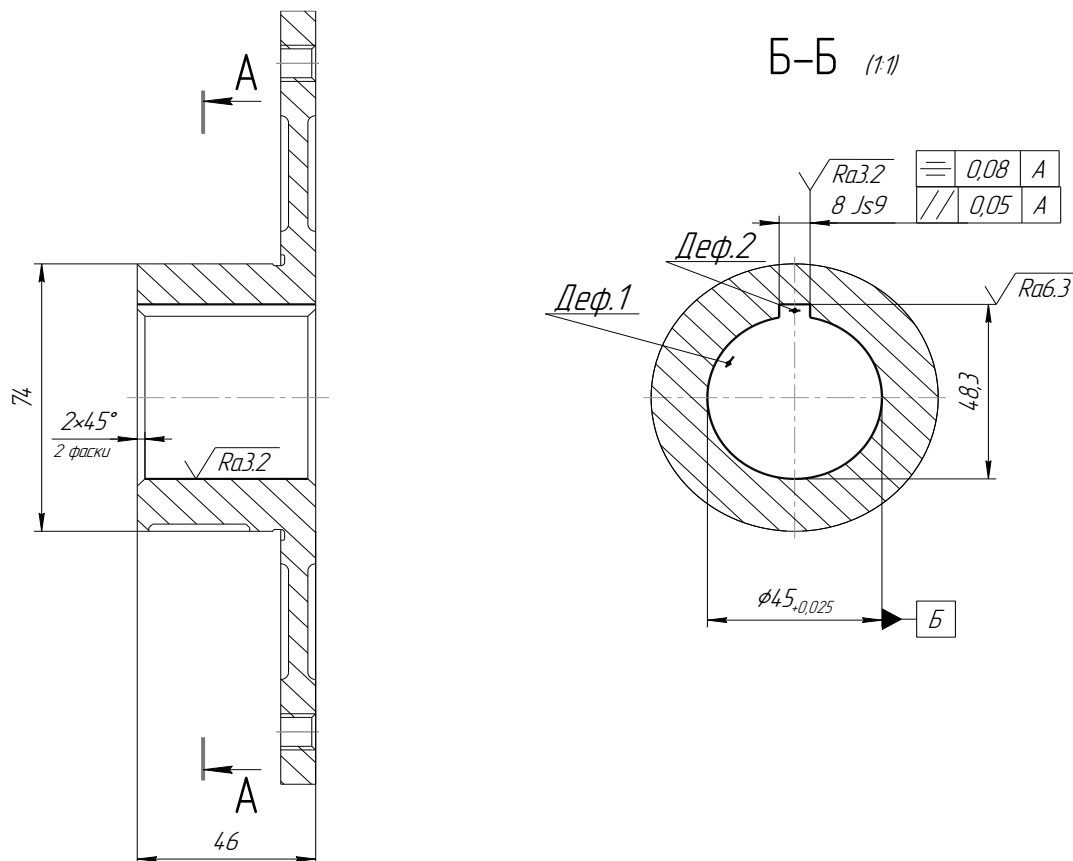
Ескіз ремонтного креслення деталі
